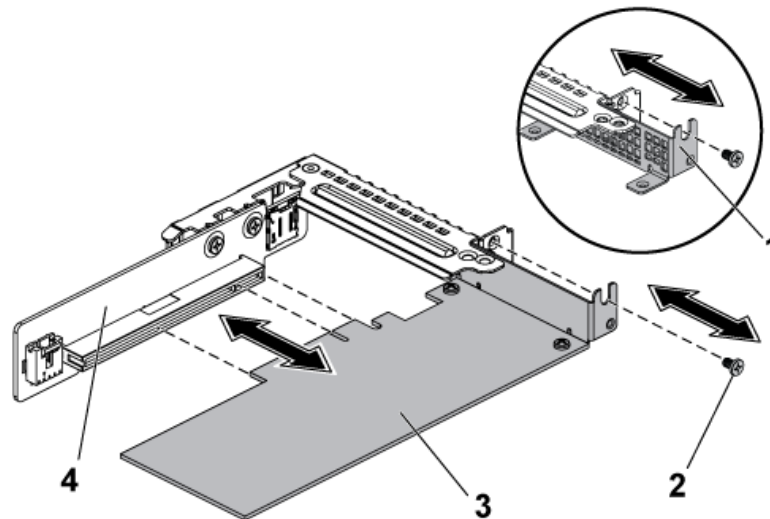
Extracción del ensamblaje de la tarjeta de expansión
